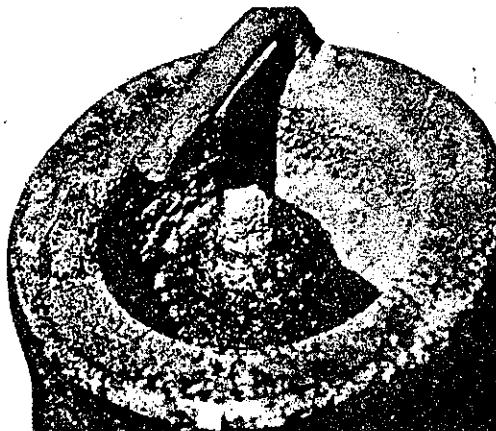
Bu şeildeki aşıntı tırnakları yanyana komşu bujilerde meydana gelir.
